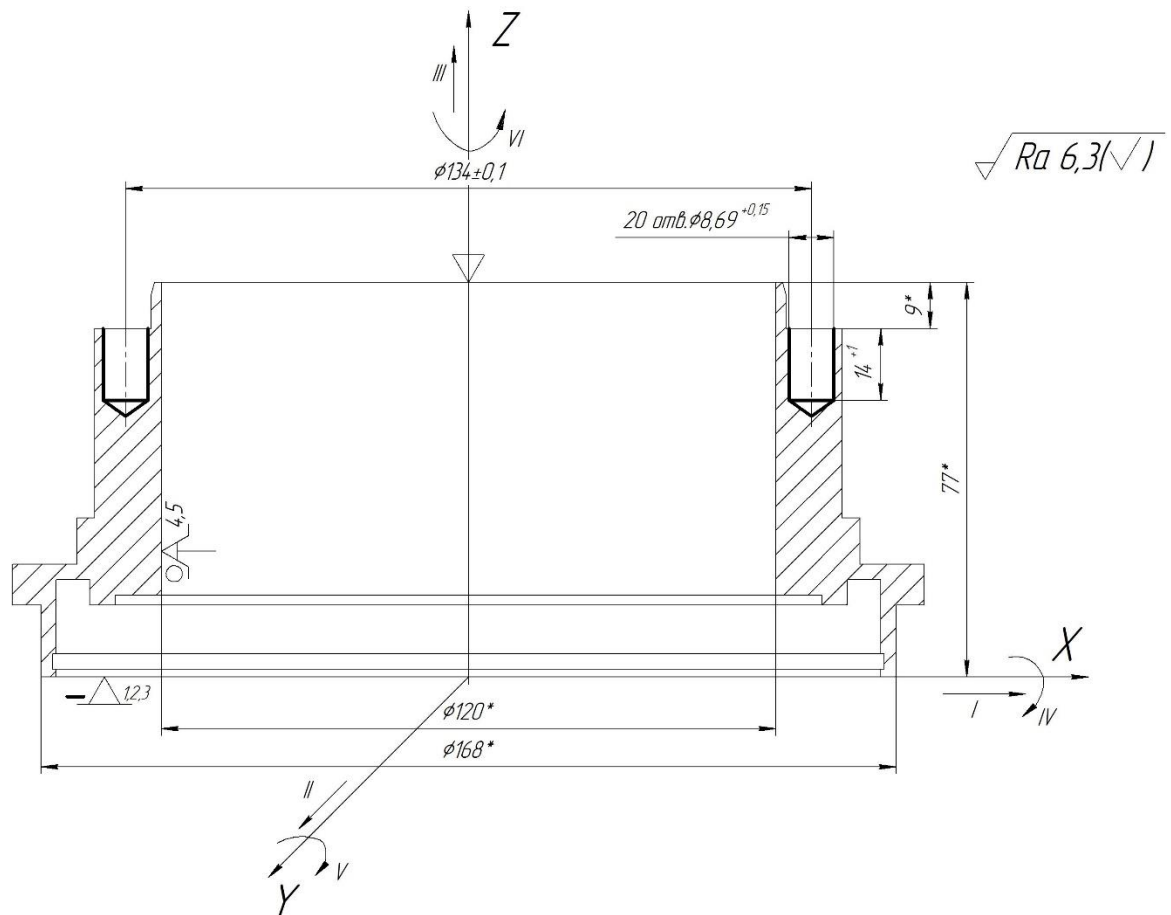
Схема базування заготовки на свердлильній з ЧПК операції
